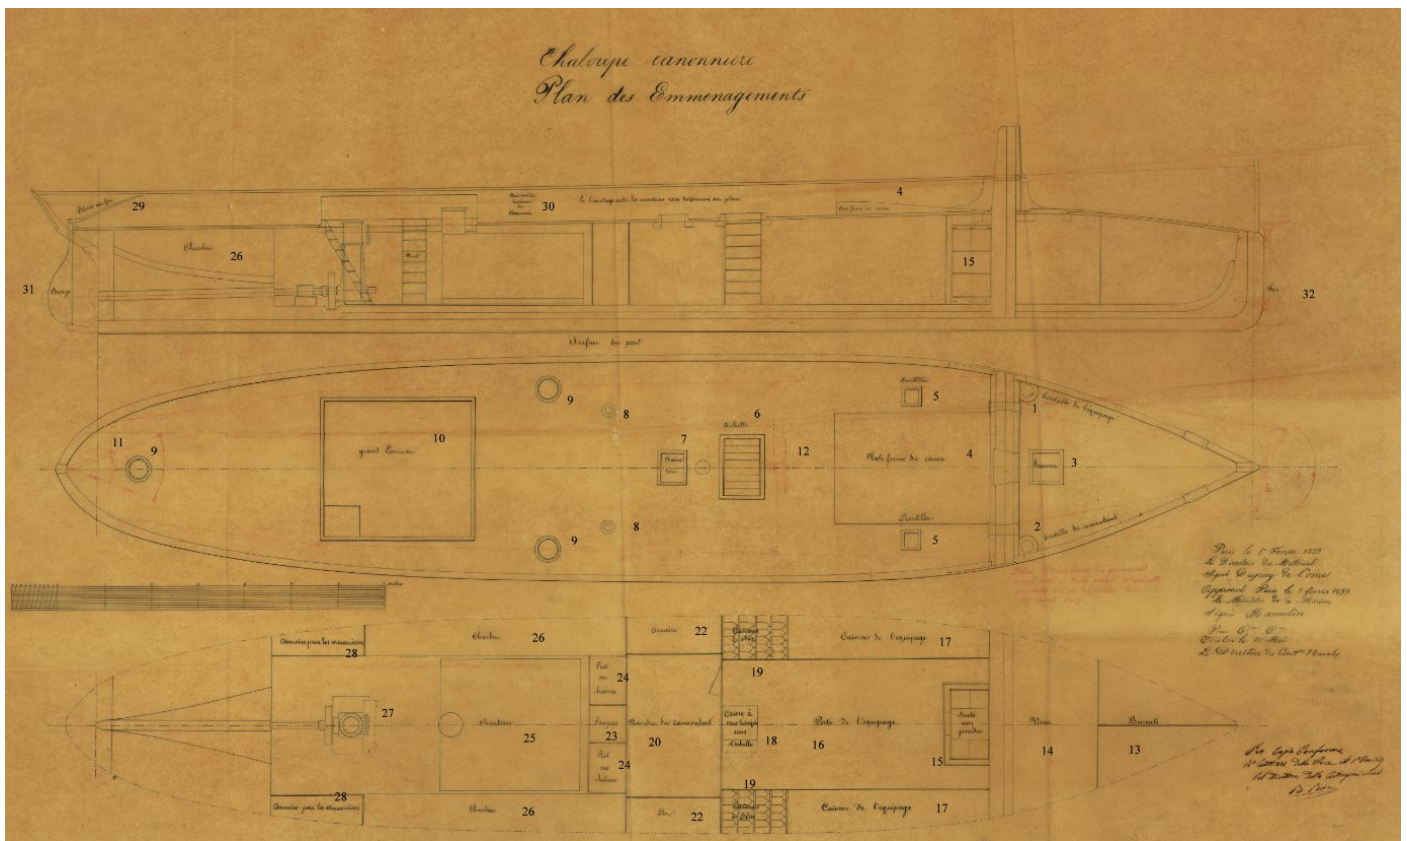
Chaloupe canonnière, Plan des Emmenagements.
